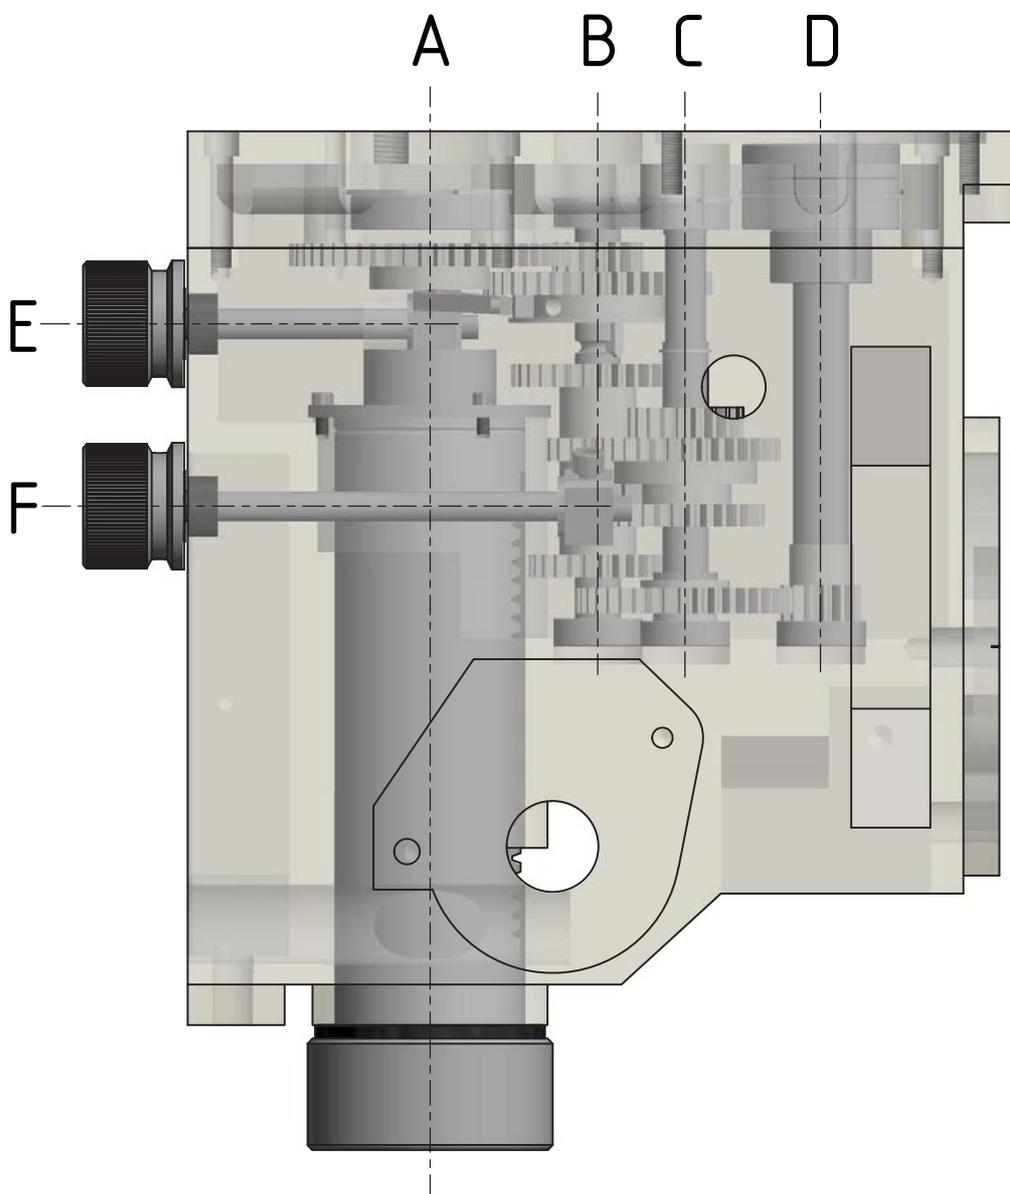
Fräskopf 1 von 6 - Milling head 1 von 6
